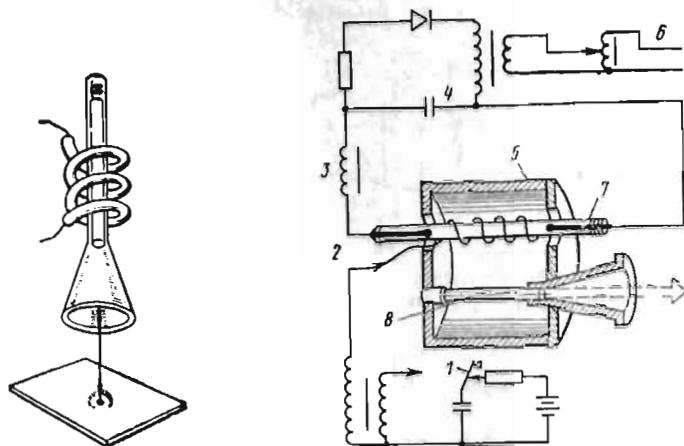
Схема излучающей головки рубинового лазера со спиральной лампой-вспышкой
